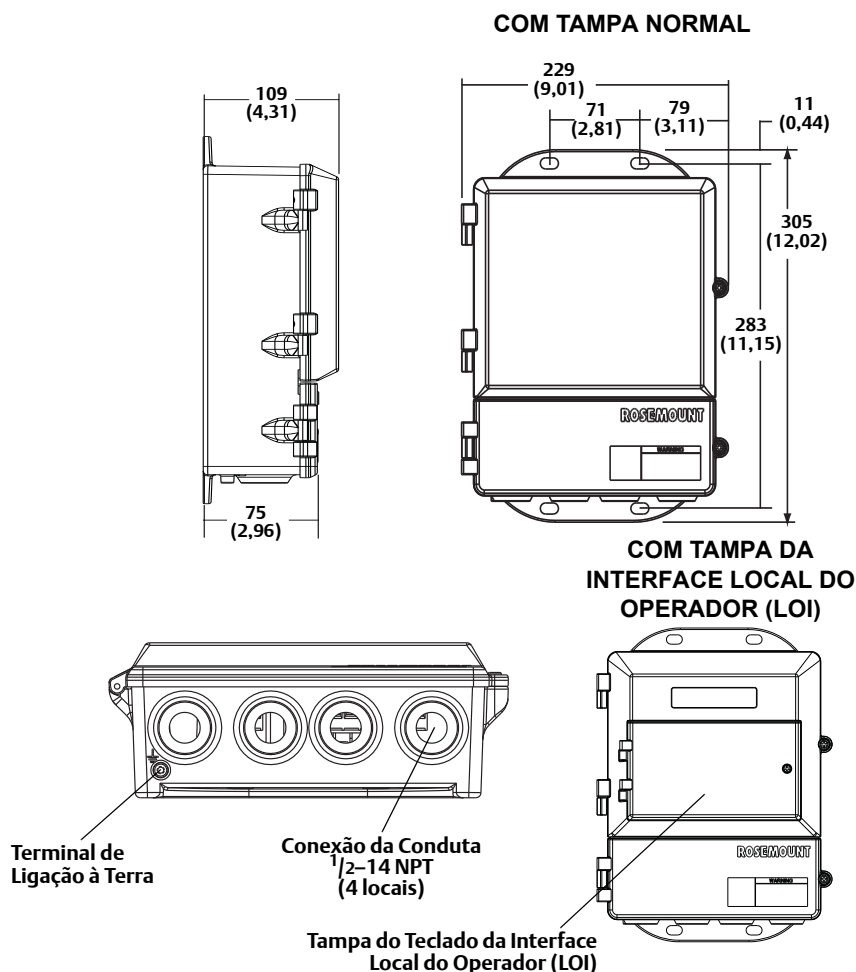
Esquema de dimensões do transmissor de montagem em campo
